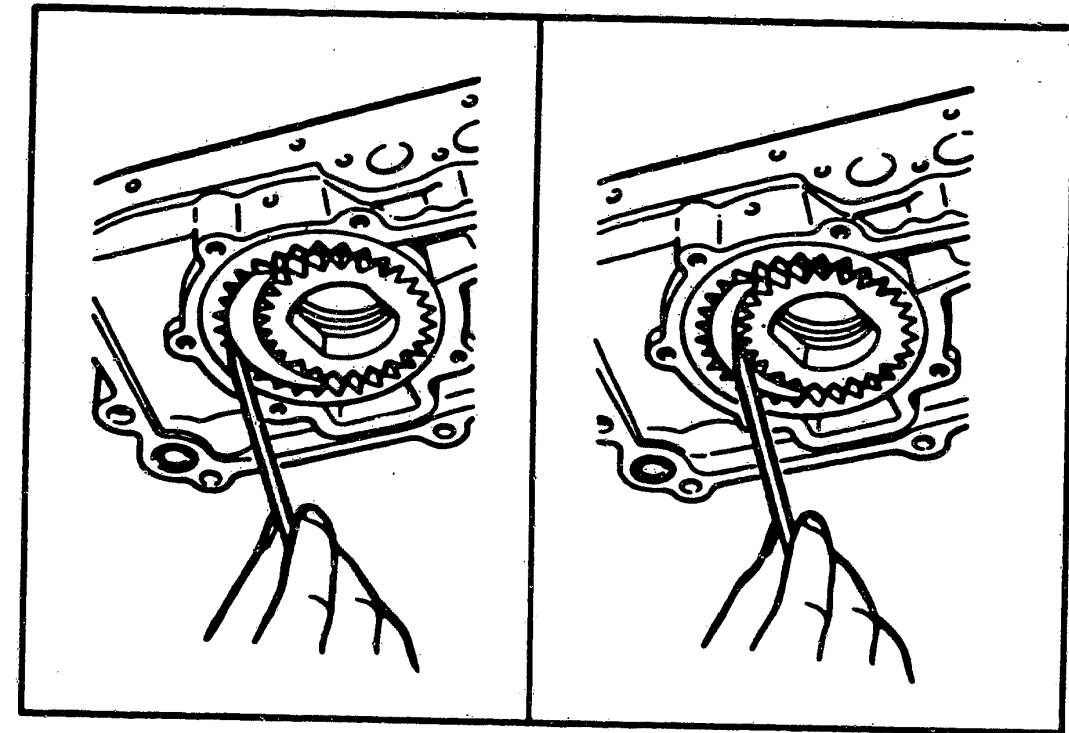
Prüfen der Ölpumpe. Die Kontrollmasse der Pumpenzahnräder sind in der Tabelle angegeben.
